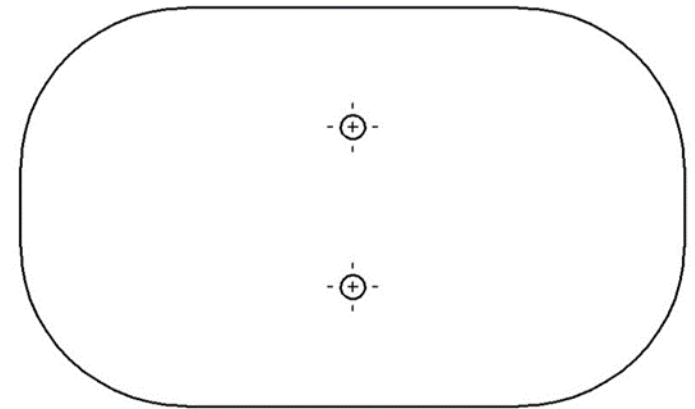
Konstrukcja metalowa ortezy na rękę i przedramię w rozłożeniu – widok wewnętrznej strony ortezy (bez przyklejonego wyścielenia)
